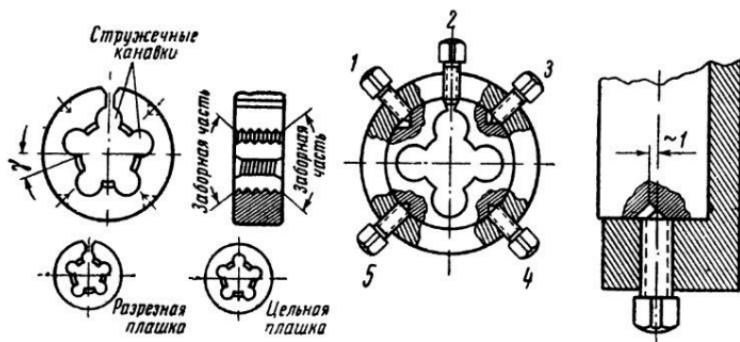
Круглые плашки и их закрепление в плашкодержателе.
